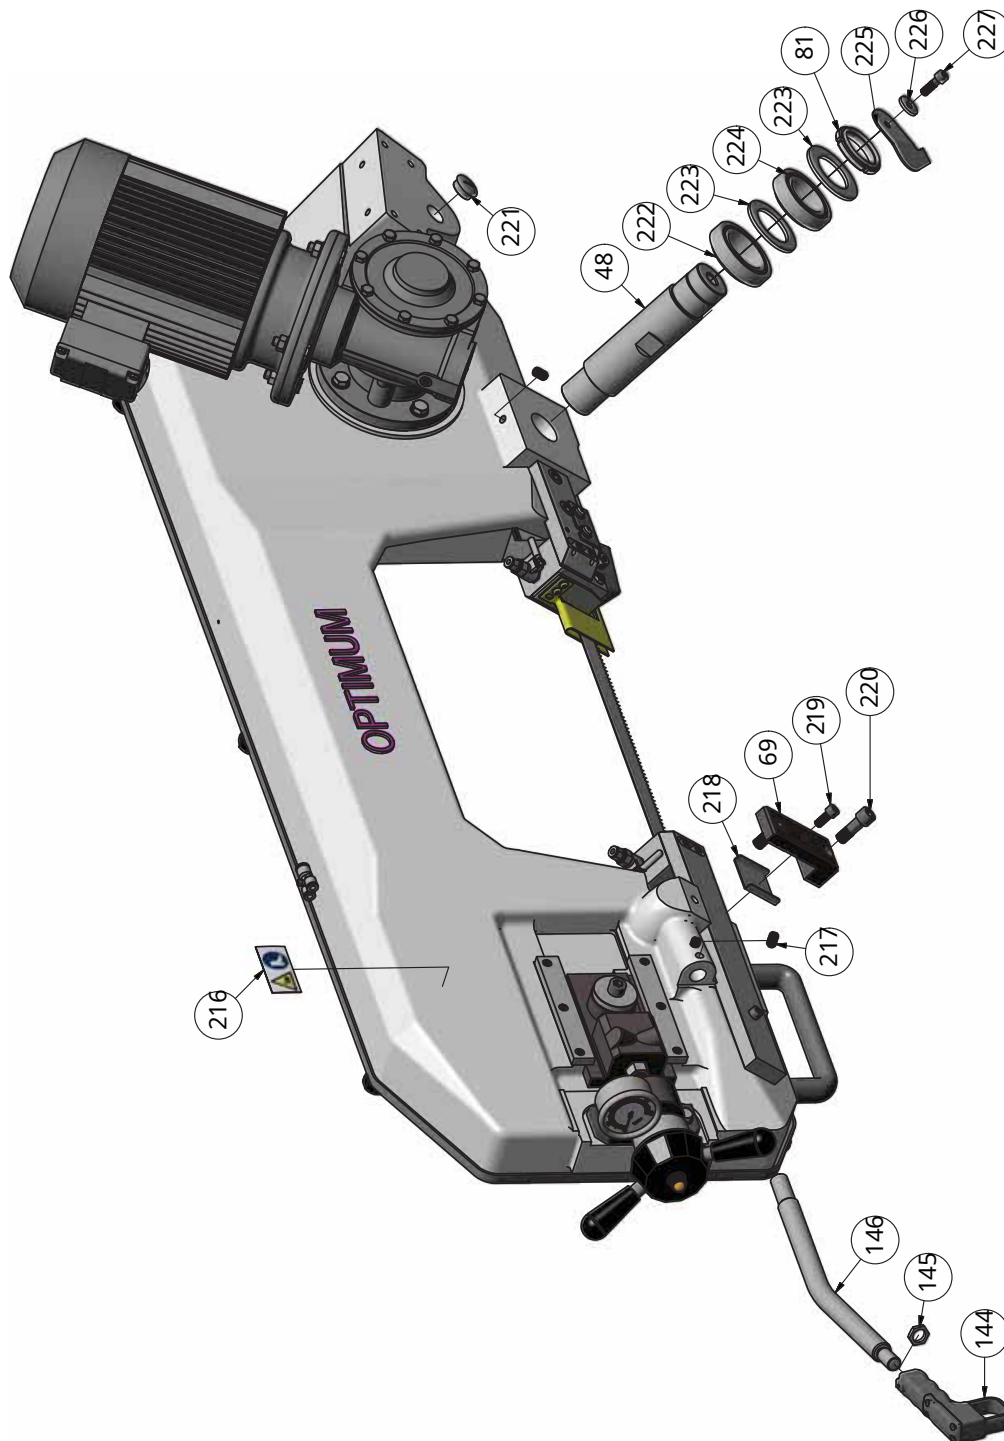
Explosionszeichnung - Dibujo de piezas de repuesto
